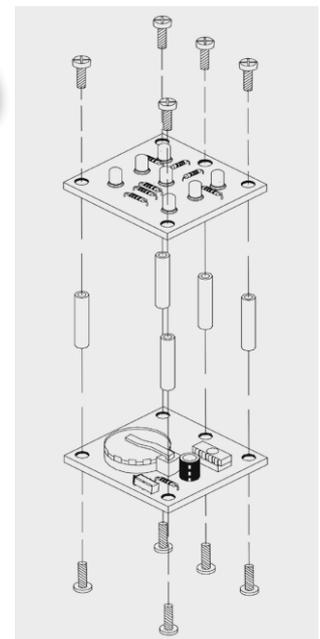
Die Explosionszeichnung zeigt das Zusammensetzen der Platinen.
